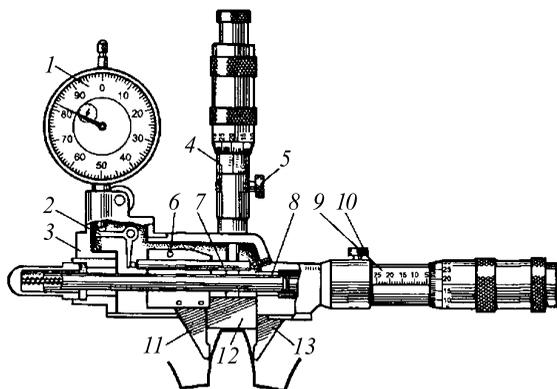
Индикаторно-микрометрический зубомер ЗИМ-16
